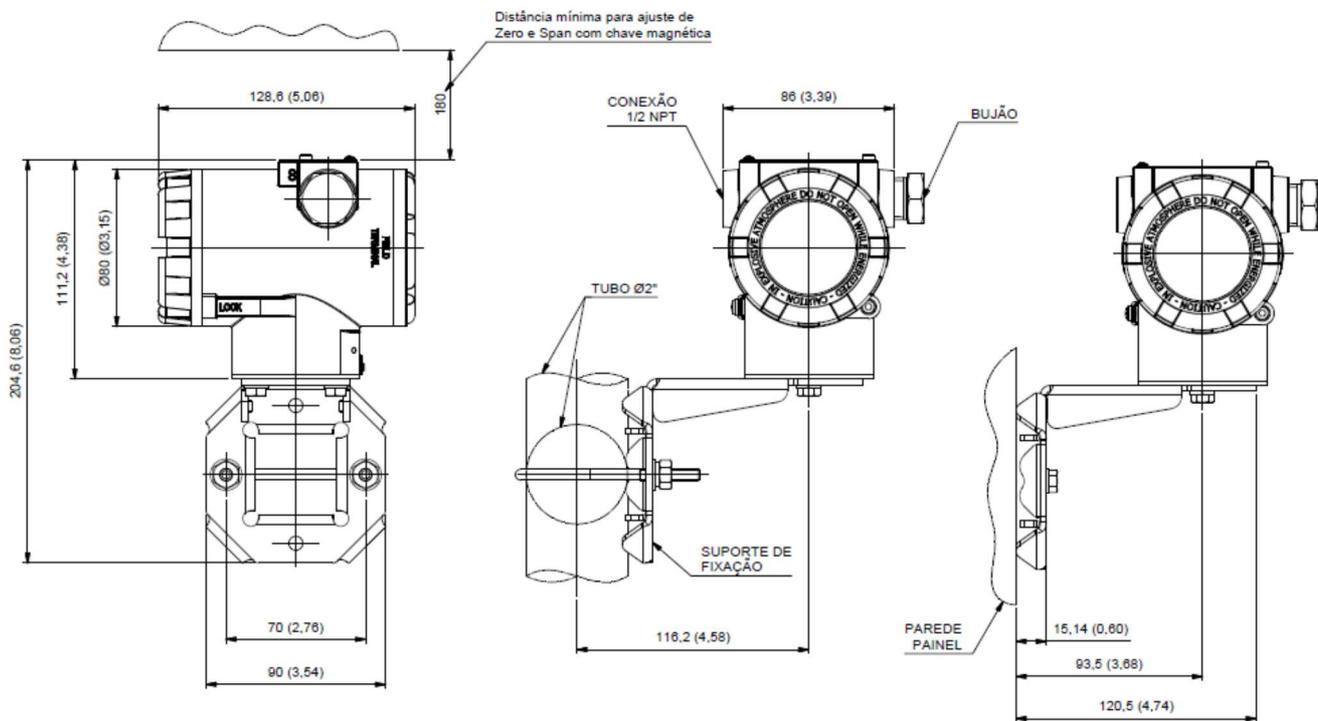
Desenho dimensional e esquema de montagem do VRI10-P.
